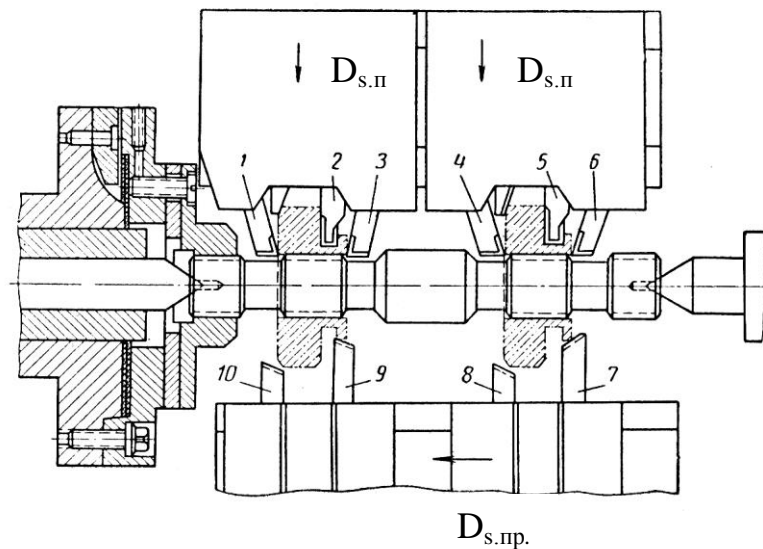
Схема обработки 2-х заготовок зубчатых колес на токарном многолезцовом станке:
